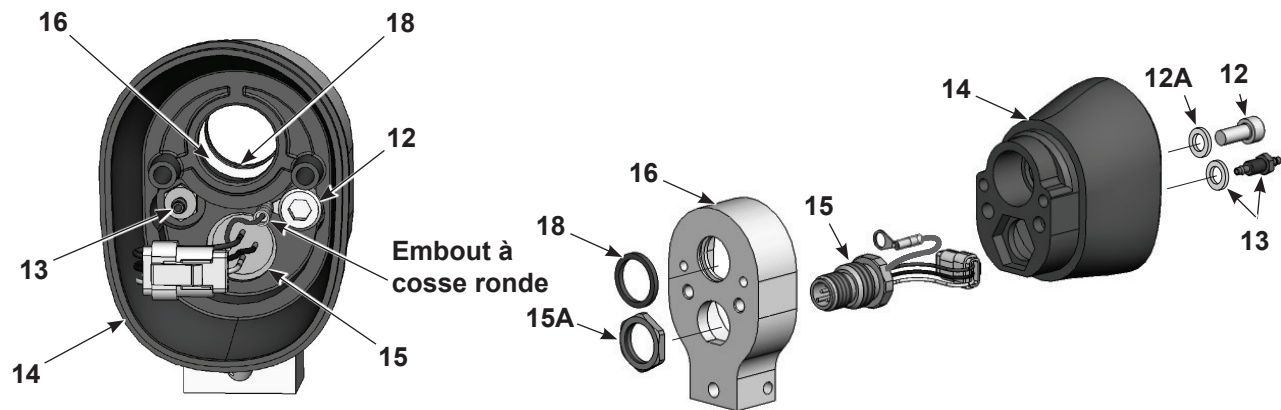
Démontage du pistolet à fixation sur barre 3 sur 3
